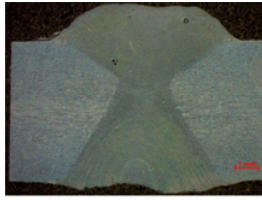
Macrographie de la soudure homogène. Le premier cordon est en dessous.
